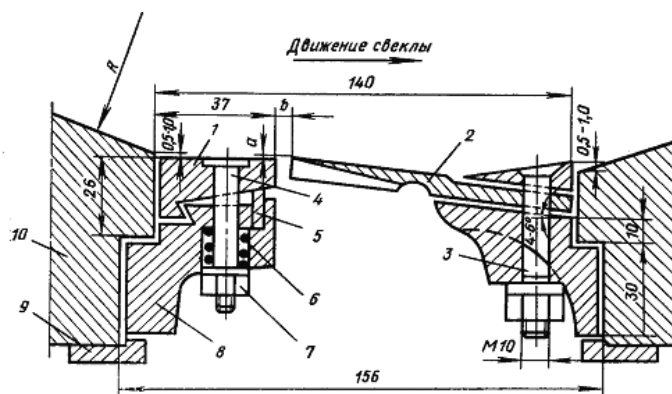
Установка рамы с ножами в корпусе центробежной свеклорезки:
